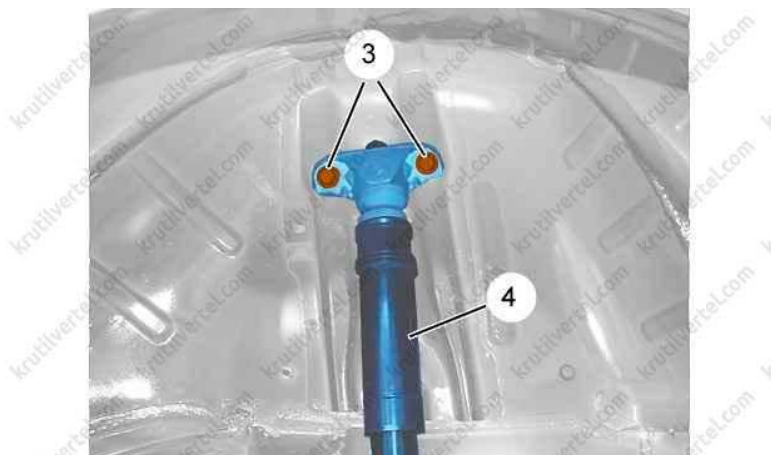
Розташування болтів 1 верхнього кріплення амортизатора
